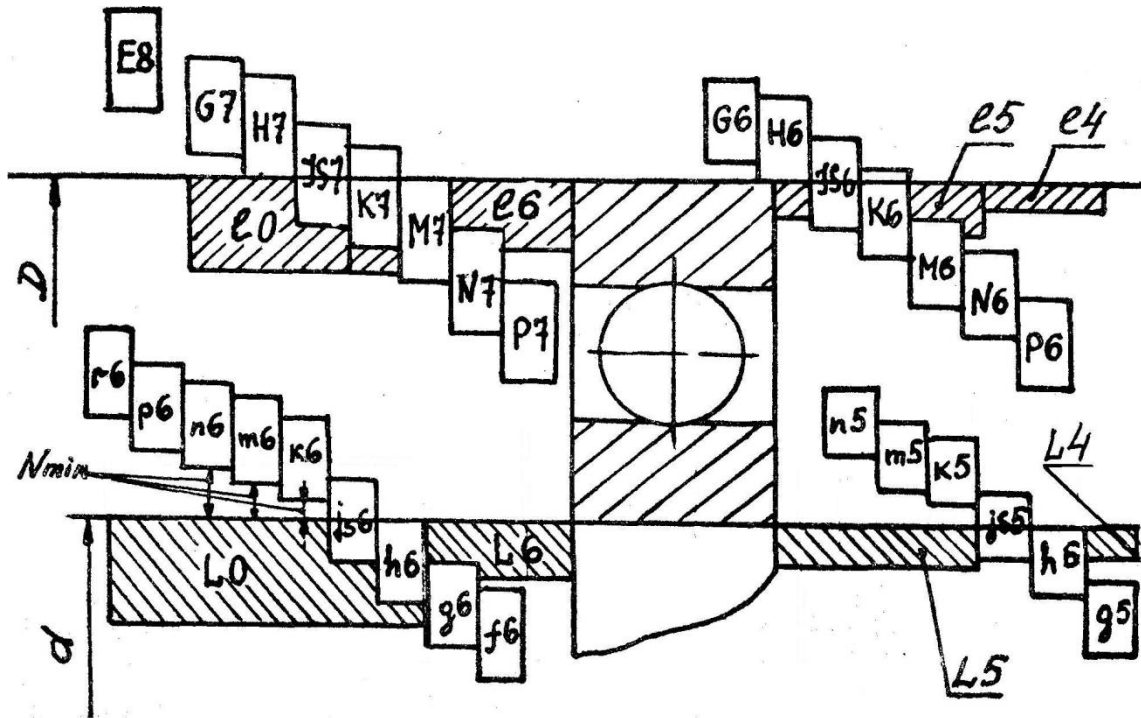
Схема розташування полів допусків підшипників кочення.
